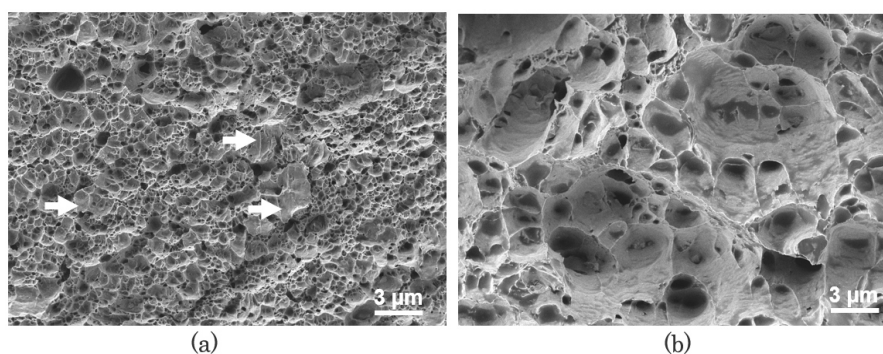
Superfícies de fratura das soldaduras de ensaios de arrancamento: (a) DLPR-65-663; (b) DLPR-56-503.
